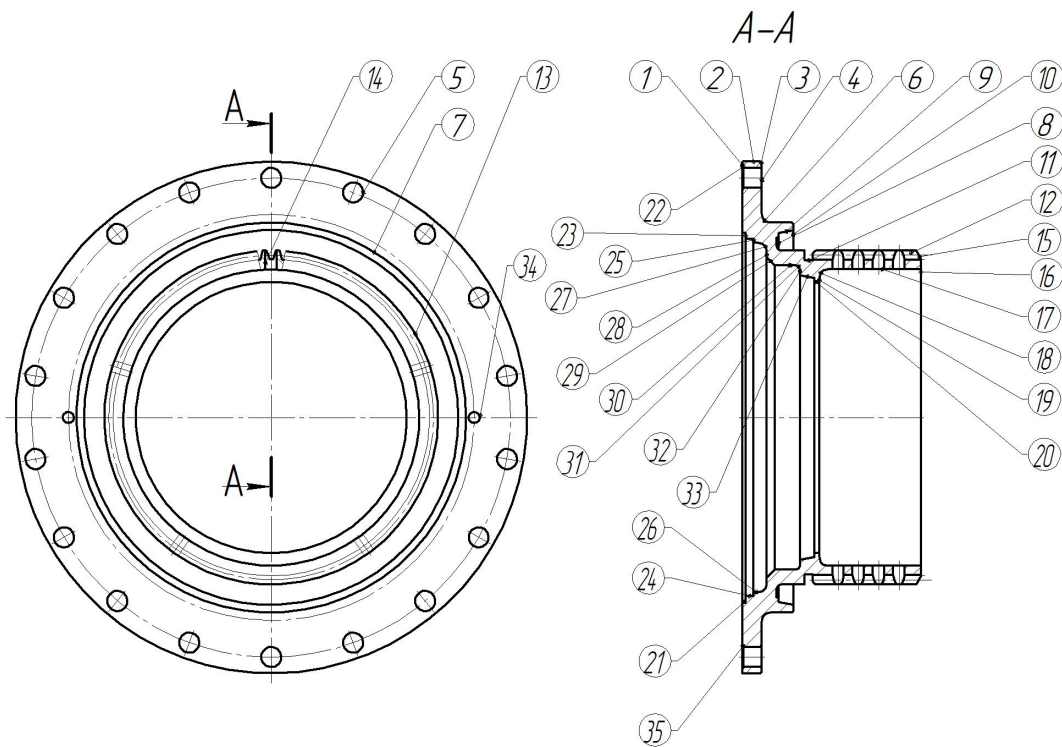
Ескіз деталі з позначеними поверхнями
